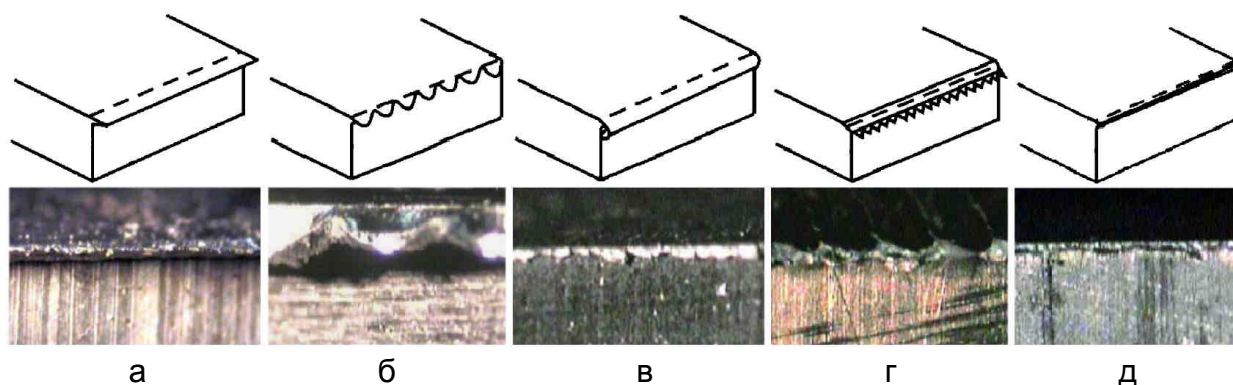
Типичные формы заусенцев, образующихся при торцевом фрезеровании [16]:
